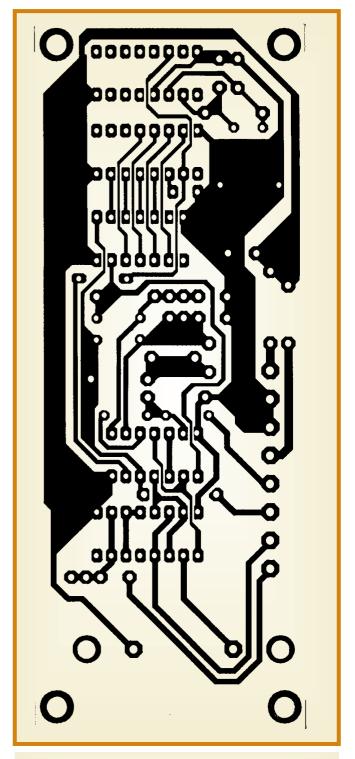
Lado del cobre de la plaqueta principal.
